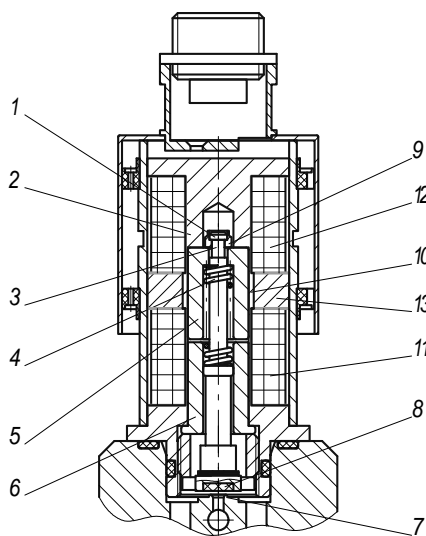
Конструктивна схема пневматичного клапана з двопозиційним поляризованим електромагнітним приводом: 1 – головка штока; 2 – корпус електромагніта (верхній стоп); 3 – шийка штока; 4 – буферна пружина; 5 – повзун (якір); 6 – нижній стоп; 7 – сідло; 8 – золотник; 9 – стопорна шайба; 10 – розподільна трубка; 11 – обмотка закриття; 12 – обмотка відкриття; 13 – постійний магніт
